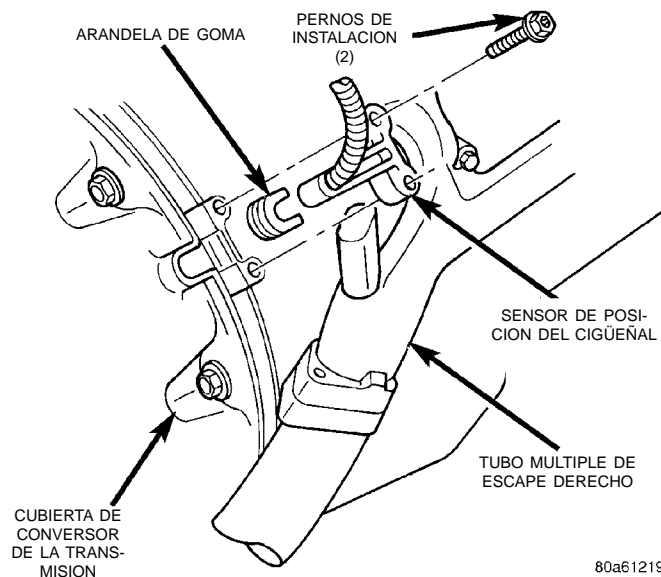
Sensor de posición del cigüeñal—Motor de 5.2L/5.9L
